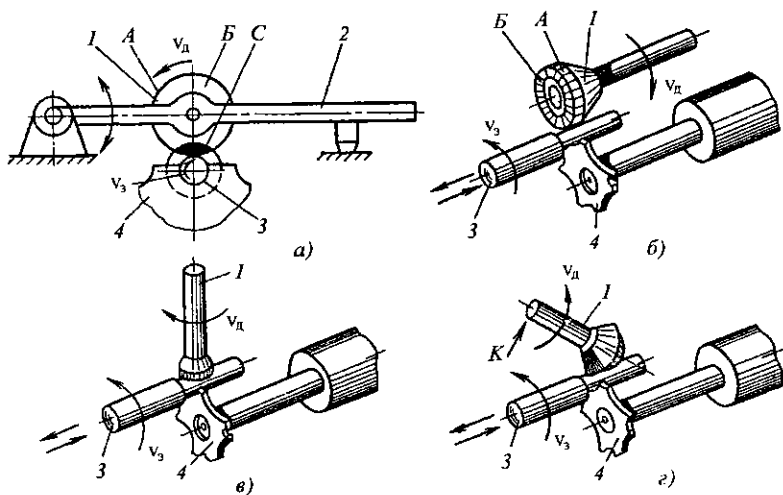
Схемы доводки цилиндрических и торцевых поверхностей цапф твердосплавными дисками с расположением осей шпинделей заготовки и твердосплавного диска: а и б – параллельным; в – взаимно-перпендикулярным; г – взаимно-наклонным
